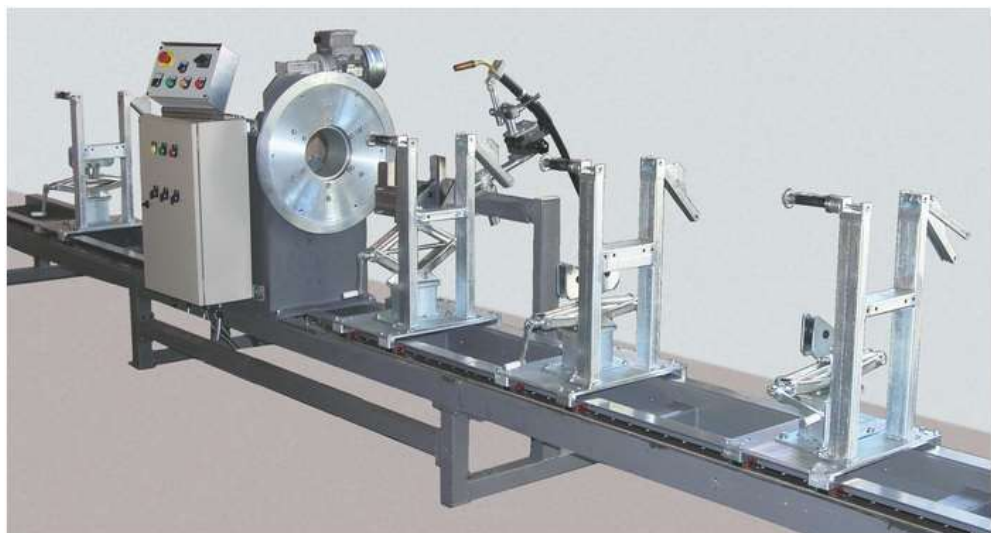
Установка для автоматичного зварювання кільцевих швів АС-391 [10]
